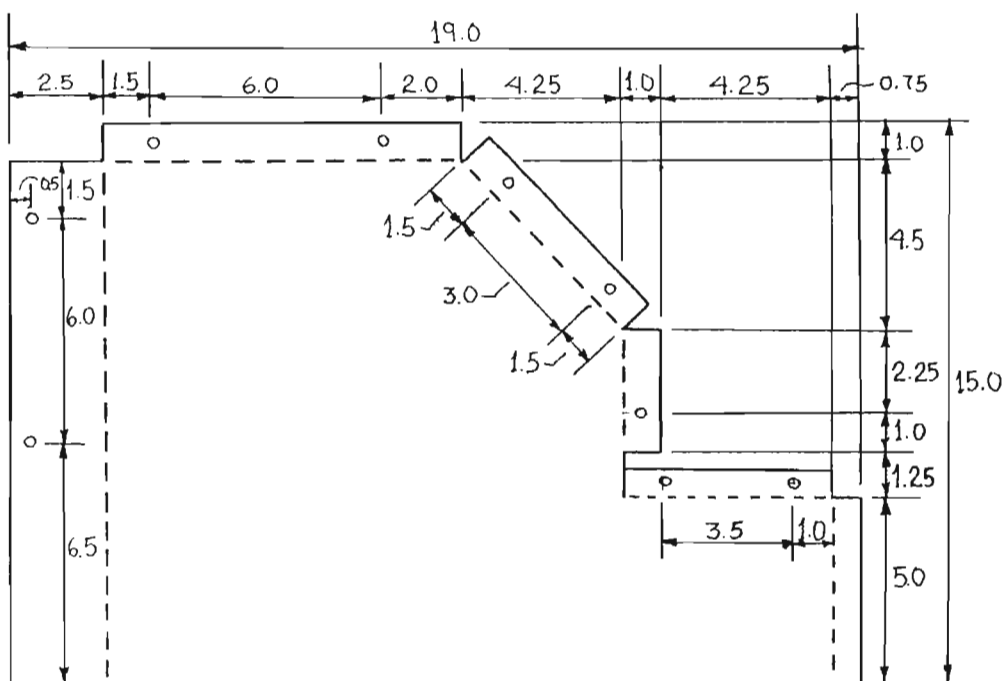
Paredes Laterales desplegadas en un plano.
